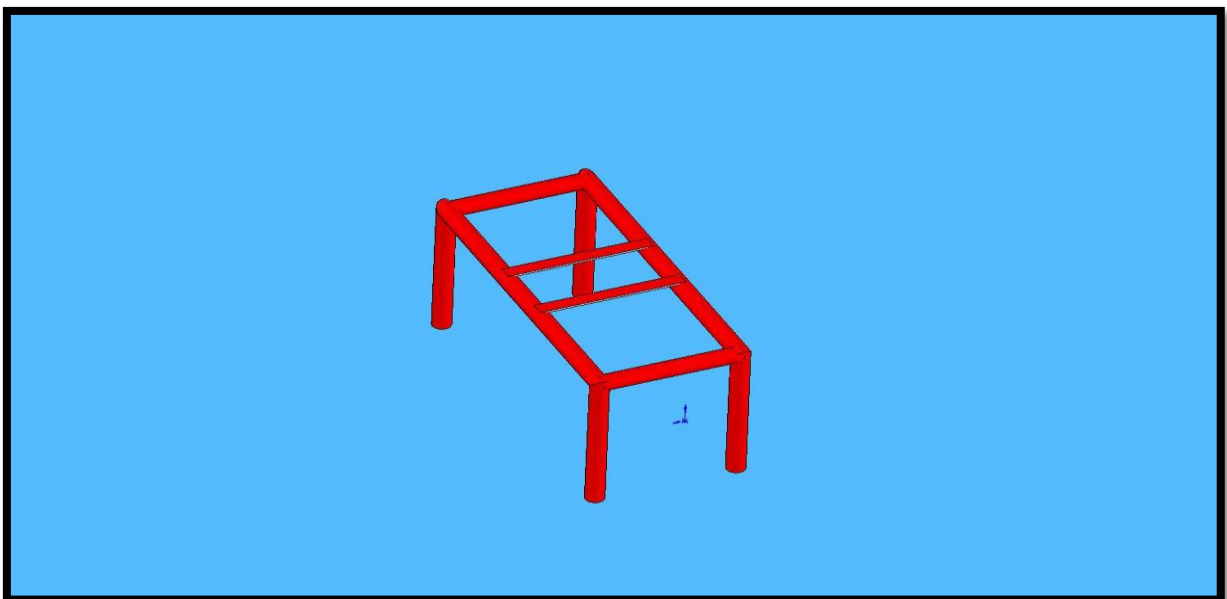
Soporte del Motor en SolidWorks vista del lado izquierdo
